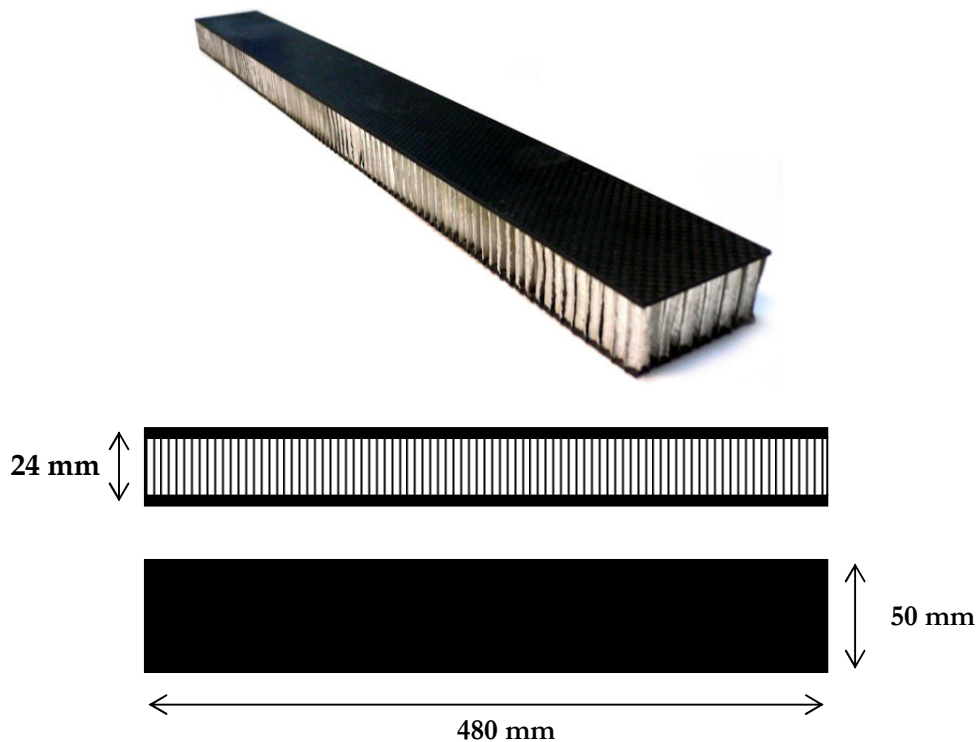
Geometría de las vigas sándwich a ensayo.
